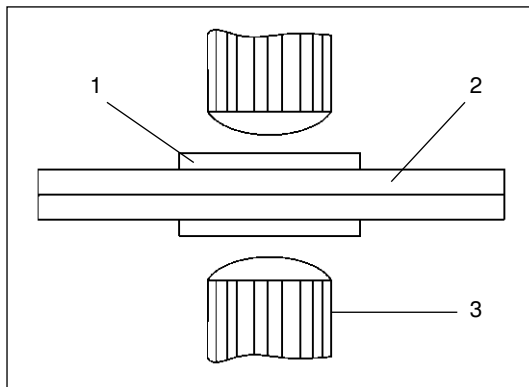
Типы соединений при точечной сварке алюминия и его сплавов
